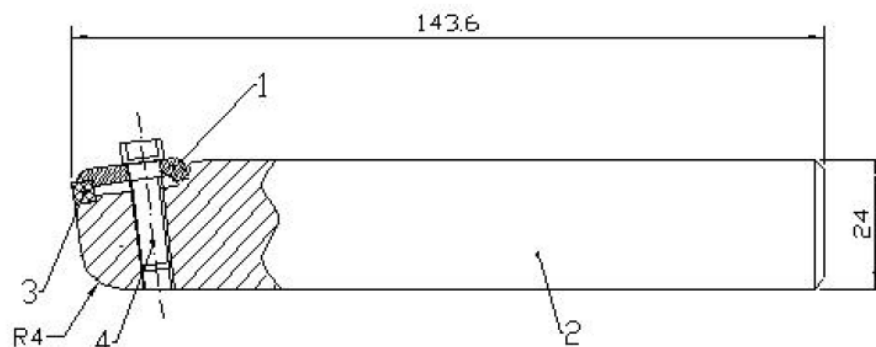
Porta Ferramenta utilizado para realização dos ensaios de torneamento: 1– arruela de fixação; 2 – suporte; 3 – composto de cBN; 4 – parafuso de Fixação.
